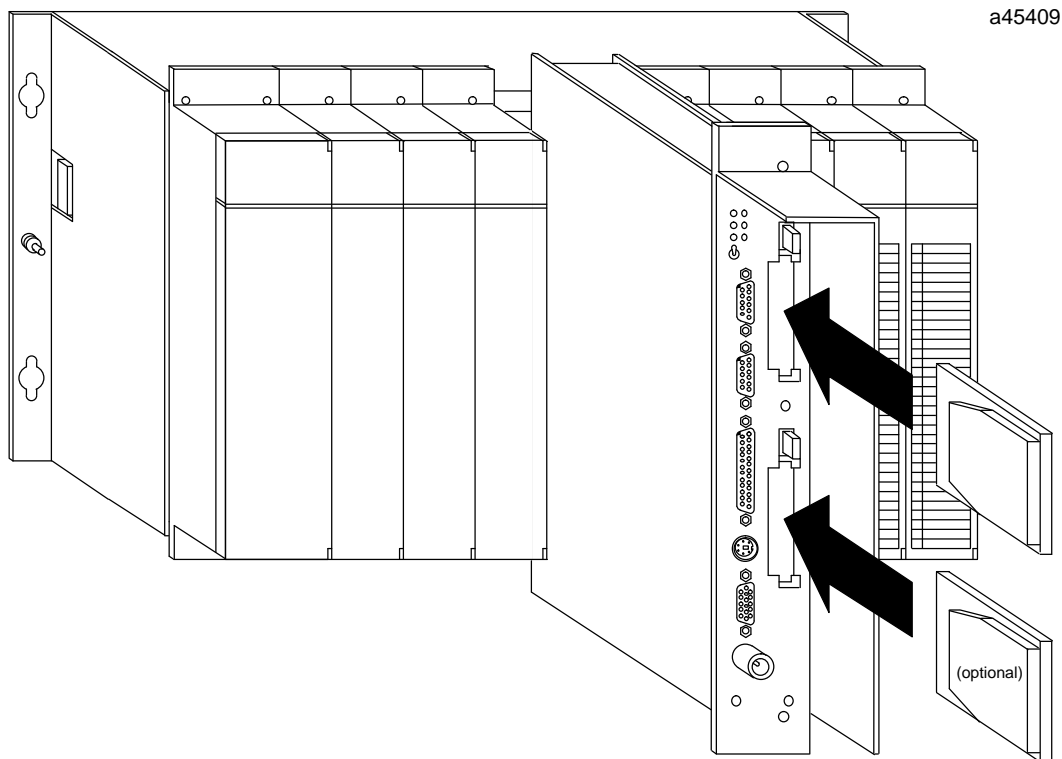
Plug & Play PC in einem SPS-Chassis der Serie 90-70
